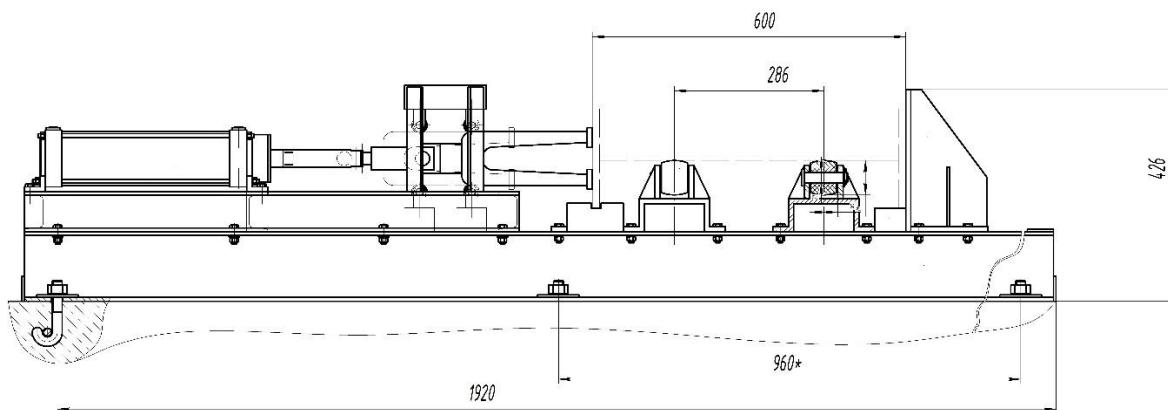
Складально-зварювальний стенд для виготовлення балок
